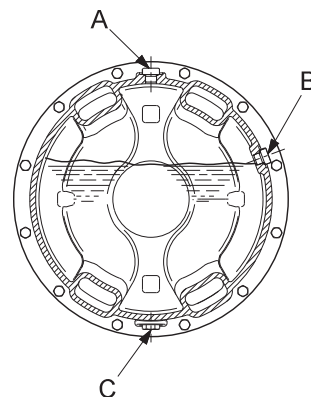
Насос с контрольной резьбовой пробкой (A) сверху
